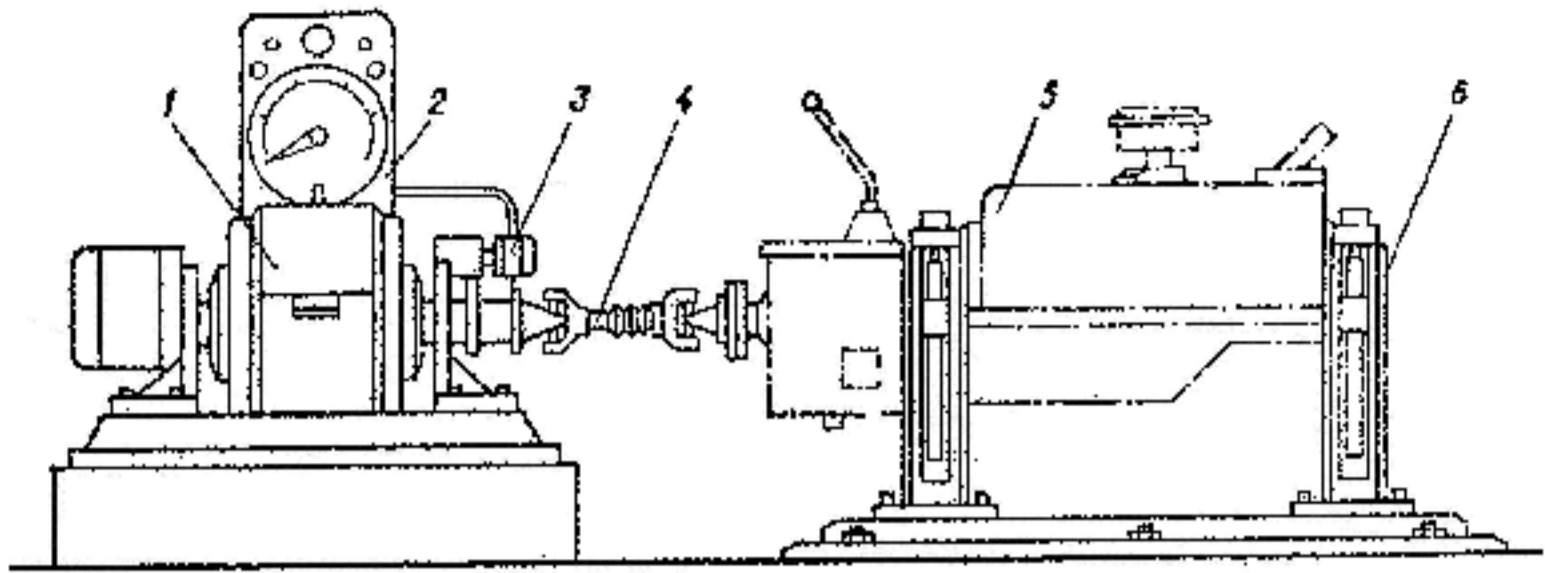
Електрогальмівний стенд для припрацювання і випробування двигунів: 1 - асинхронний електродвигун; 2 - щиток з приладами; 3 - привод тахометра; 4 - з'єднувальний шарнірний вал; 5 - випробувальний двигун; 6 - стояки (4 шт.) для встановлення двигуна
